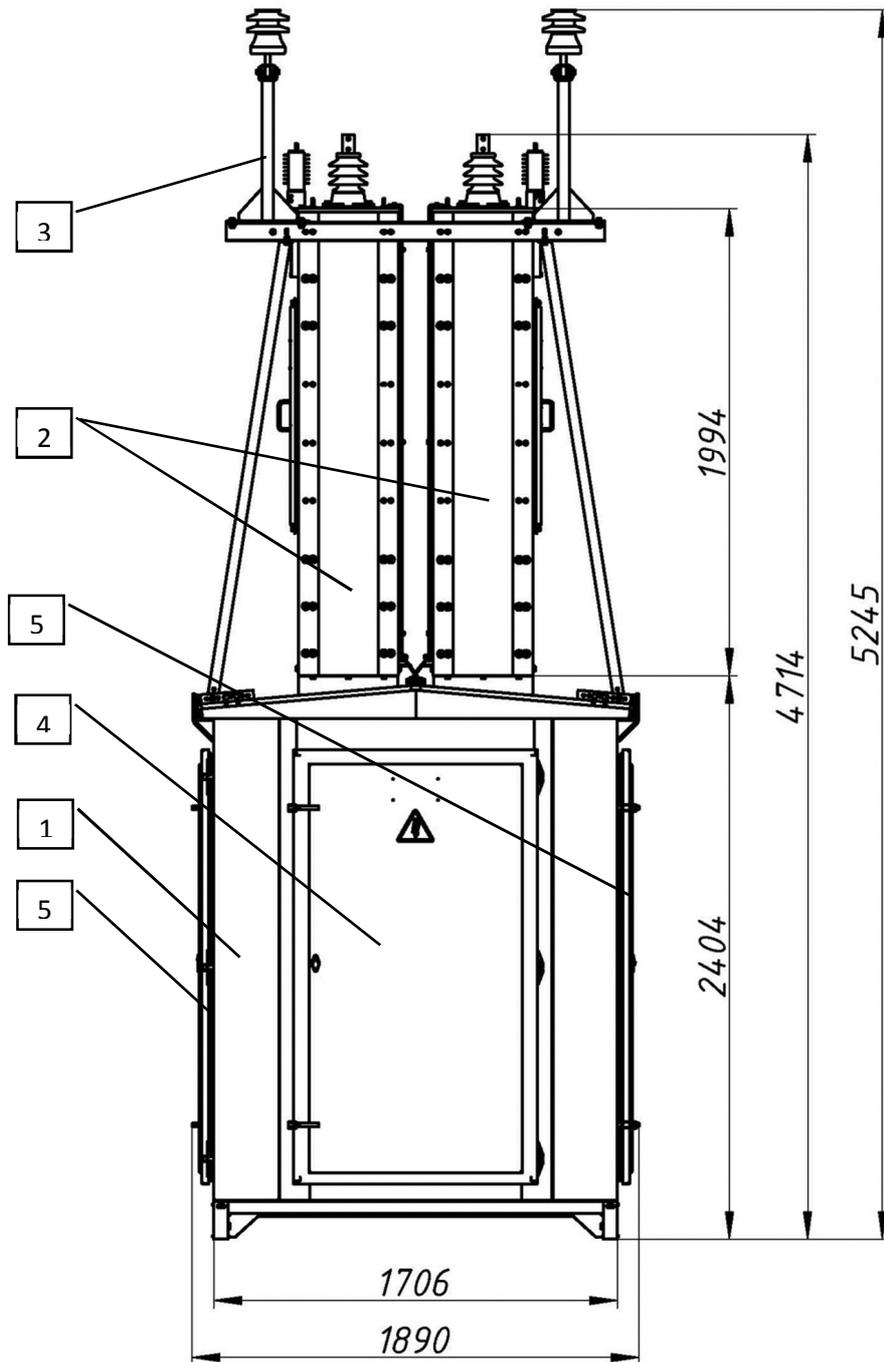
Отсек РУНН КРУН-СВЛ-МЭТЗ (наружная дверь скрыта)
